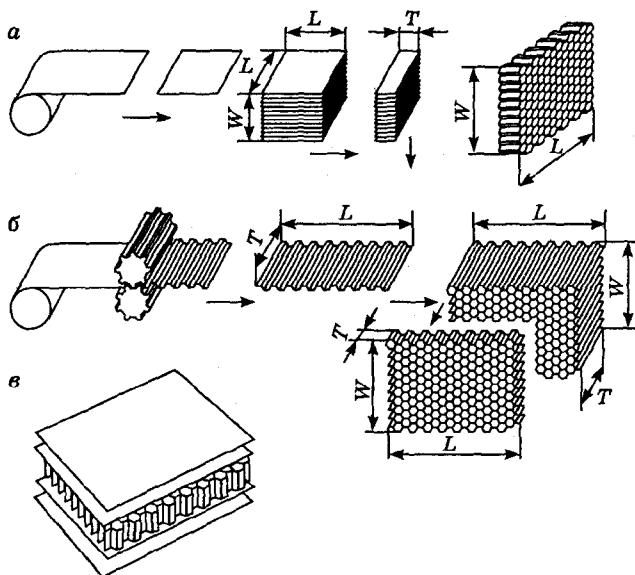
Схема изготовления наполнителей (а, б) и вид сотовой конструкции (в)
